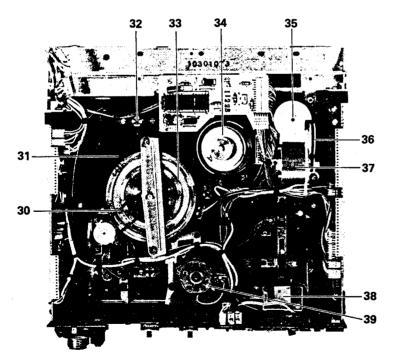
Unteransicht Fig. 1-5 Bottom view
